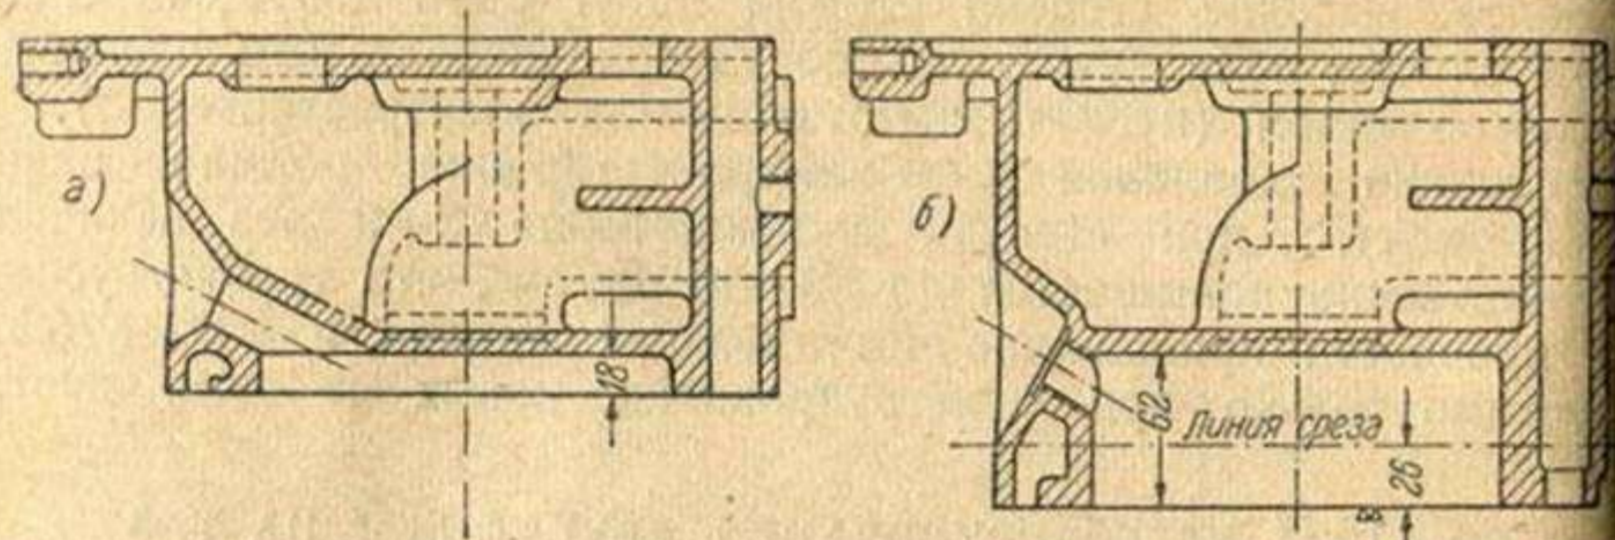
Газовая (а) и лигроиновая (б) головки цилиндров двигателя ЧТЗ-60
